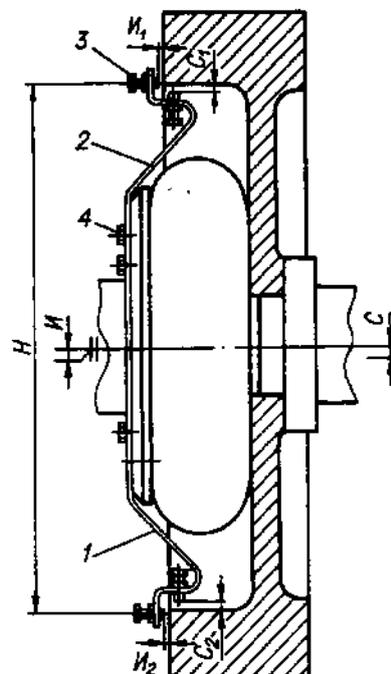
Схема центровки коленчатого вала дизеля и вала генератора:
